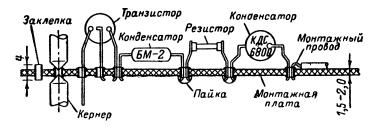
Установка монтажных заклепок и закрепление деталей.
